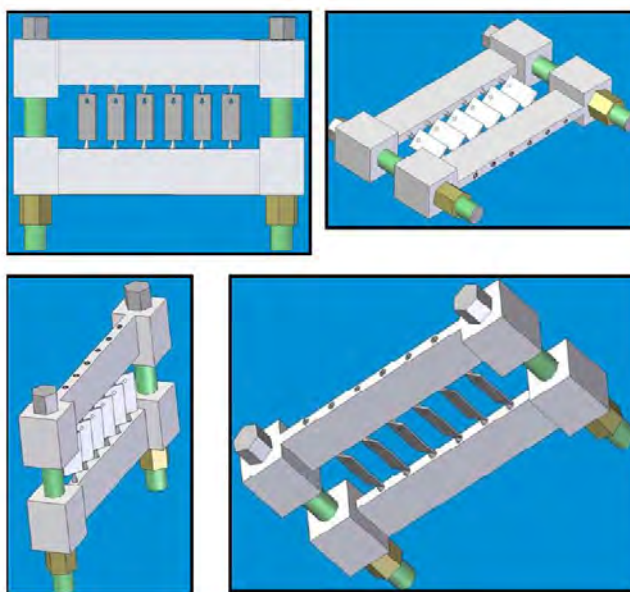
Detalle del diseño del portamuestras utilizado en el proceso de proyección térmica, fuente (Damra, 2009).
